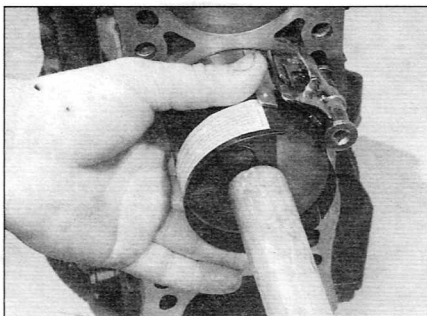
Введите поршень в цилиндр с помощью ручки молотка
